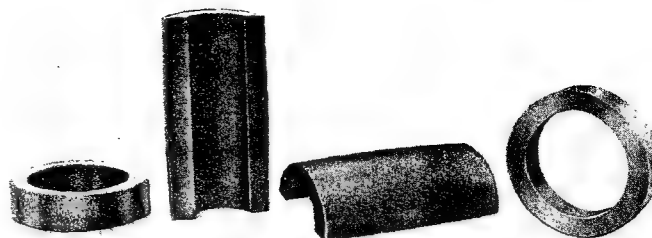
Despiece del acoplamiento de anillos (fig. II, 331).
